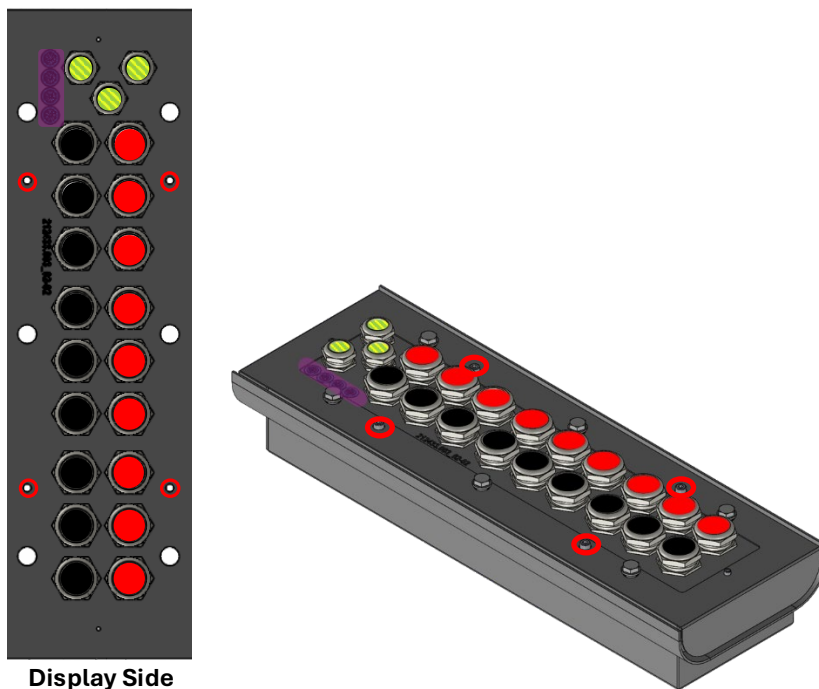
MCS-Dispenser Kabeleinführungsplatte mit Kabelverschraubungen
